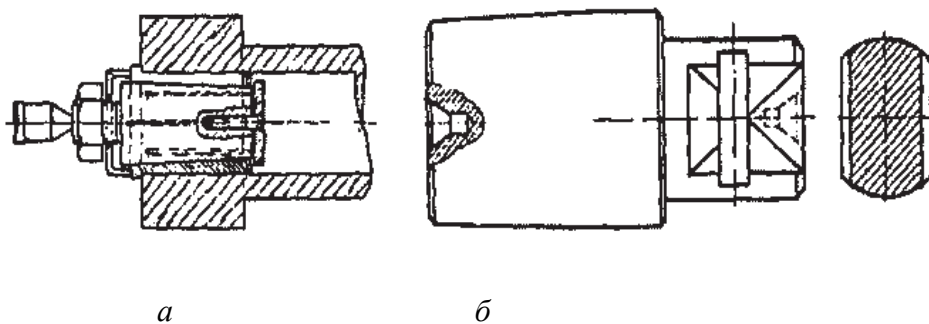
Приспособления для установки заготовок шпинделей в центрах:
